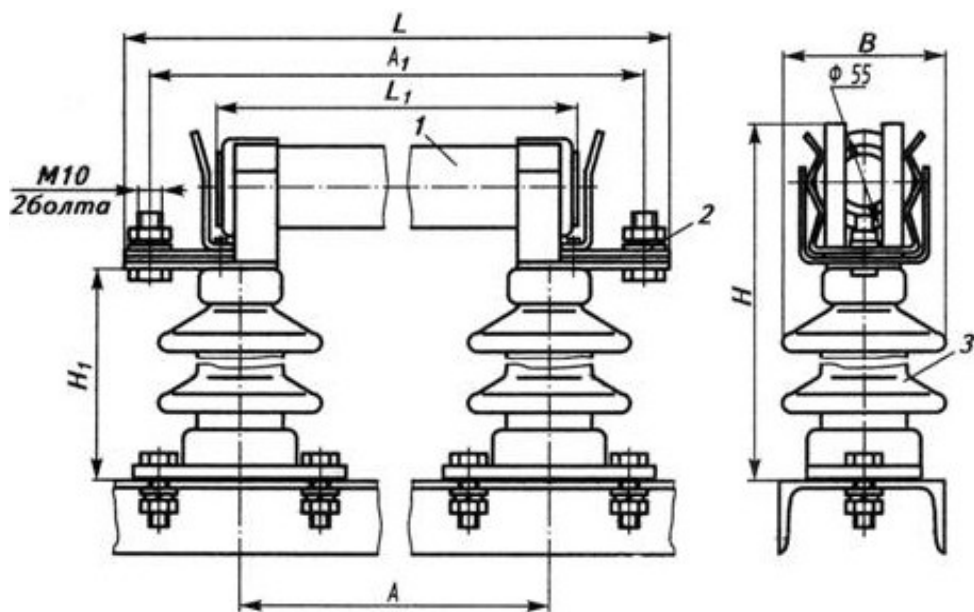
Габаритные, установочные и присоединительные размеры предохранителей серии ПКН001 (исполнение У1, ХЛ1) 1-патрон; 2-контакт; 3-изолятор
